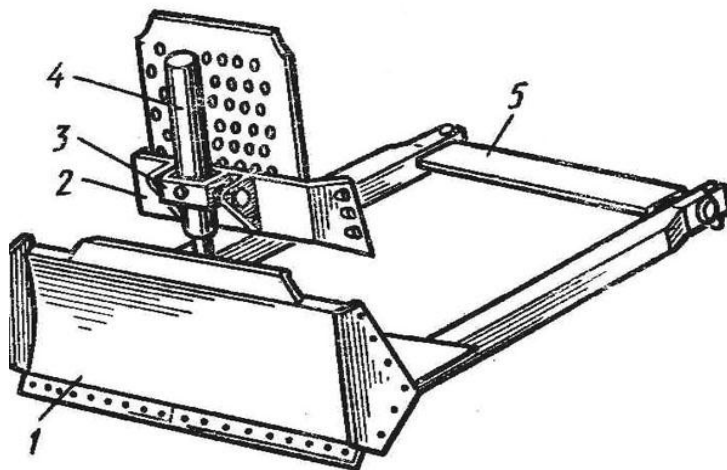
Бульдозерное оборудование с жестким креплением отвала к толкающим брусам: 1 – отвал, 2 – капот трактора, 3 – подвеска, 4 – гидроцилиндр подъема и опускания отвала, 5 – поперечная балка
